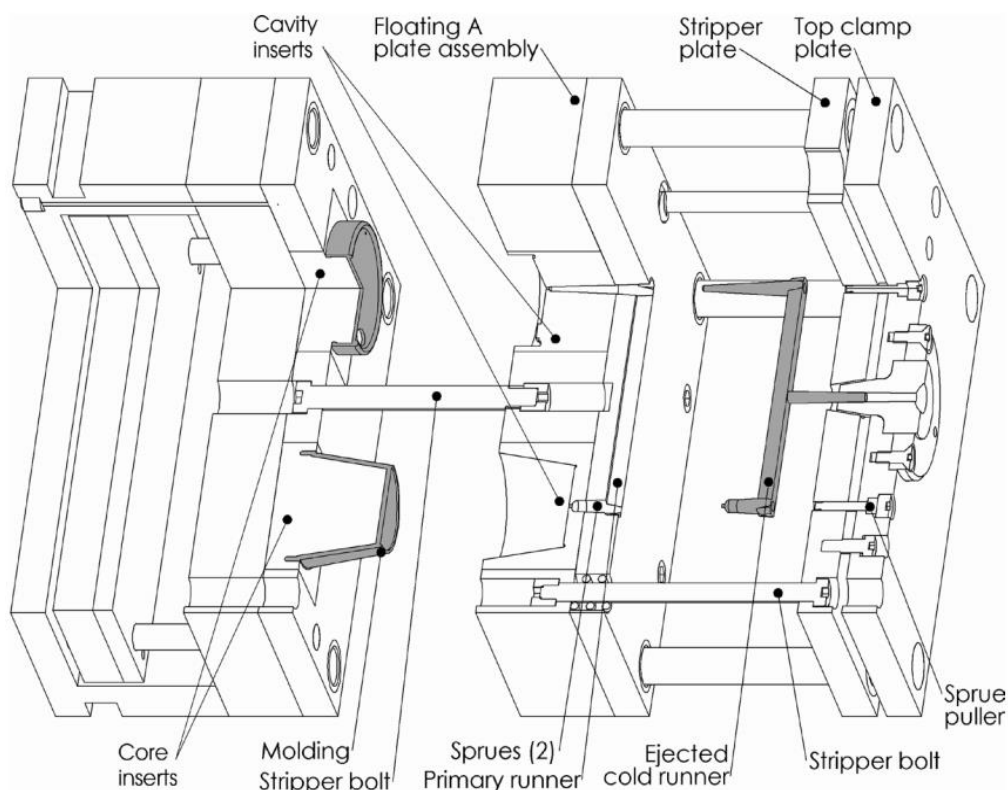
Vista seccionada de um molde de três placas durante a fase de extração [11]
